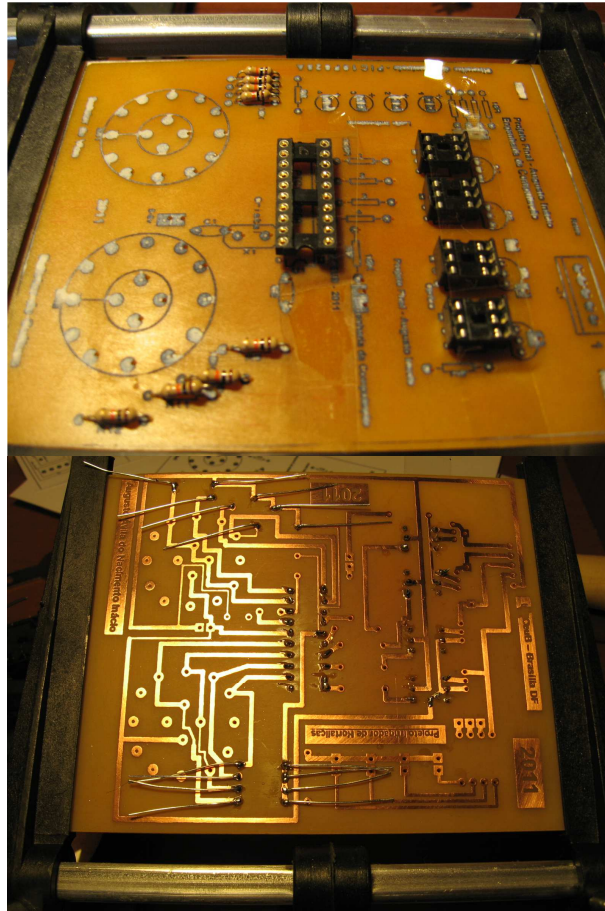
Vista superior e inferior da placa de controle em processo de soldagem e fixação dos componentes
